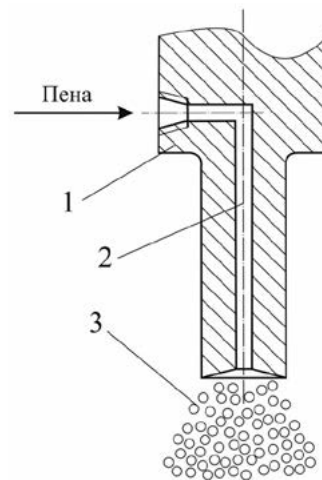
Схема излучателя для распыления жидкостей: 1 — корпус излучателя; 2 — канал для подачи жидкости; 3 — капли аэрозоля
